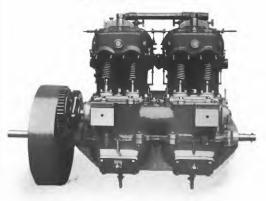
Der 4 cyl. Benz-Motor. Auspuffventilseite.
